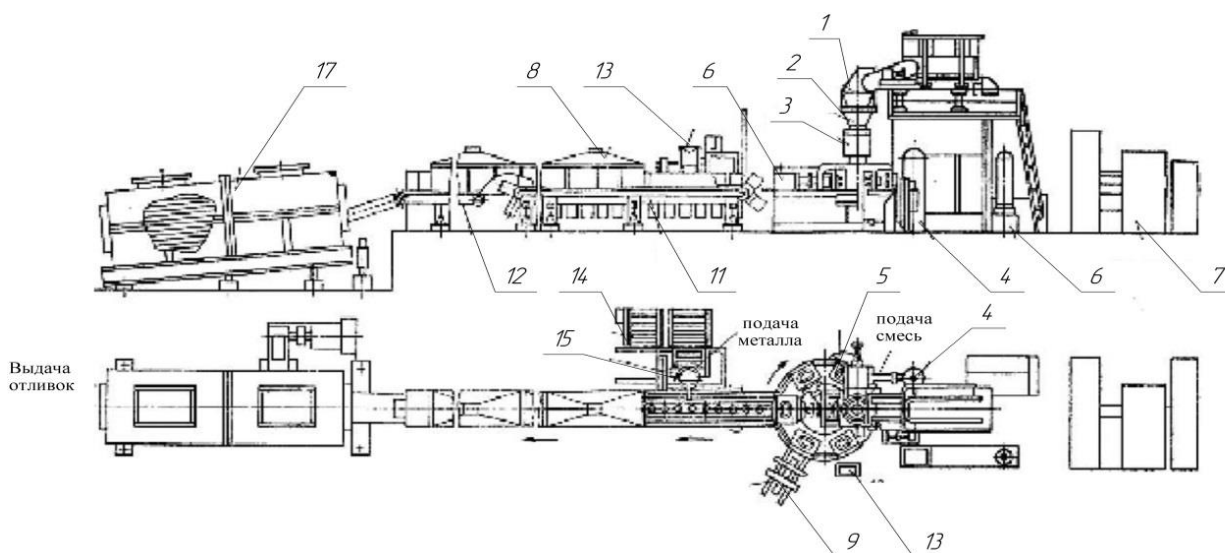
Комплексная автоматическая линия АЛ23714 безопочной горизонтально-стопочной формовки, сборки, заливки и выбивки:
